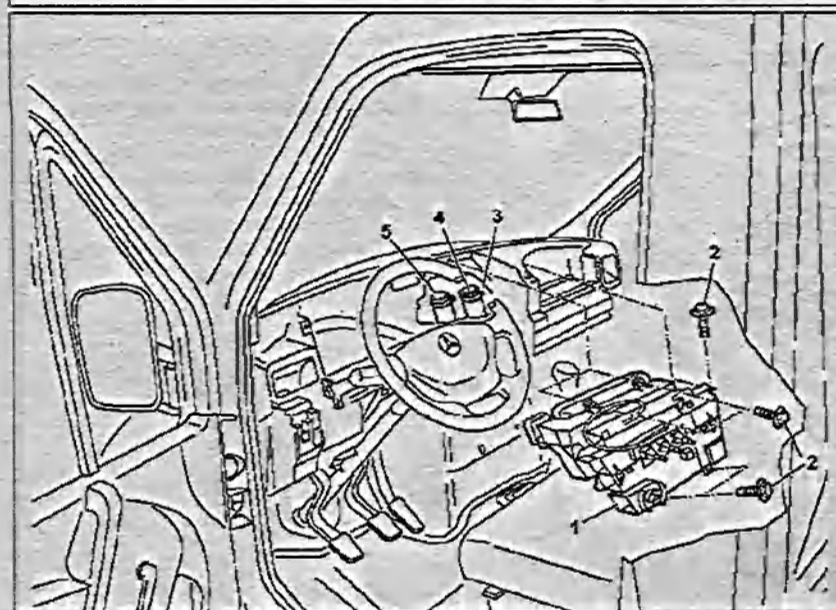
в. Снятие и установка корпуса системы вентиляции, отопления:
